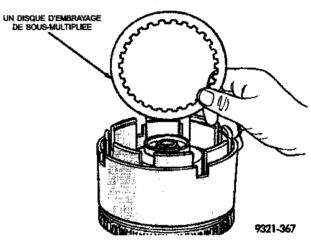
Déposer un disque d'embrayage de sous-multipliée
